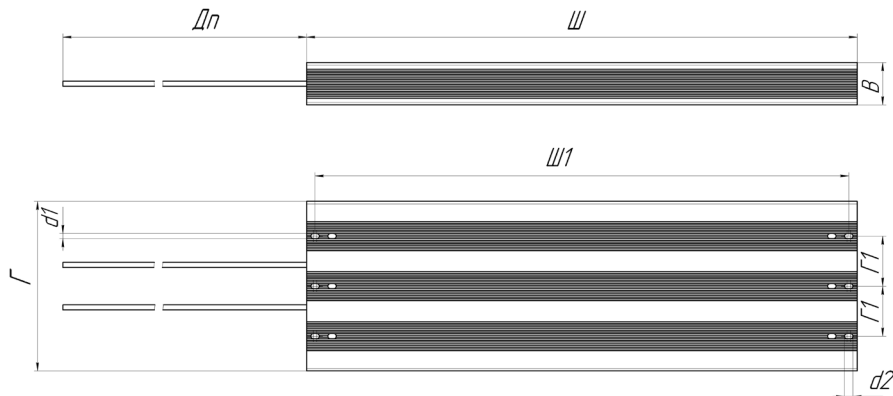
Габаритно-установочные чертежи резисторов серии IBRA
